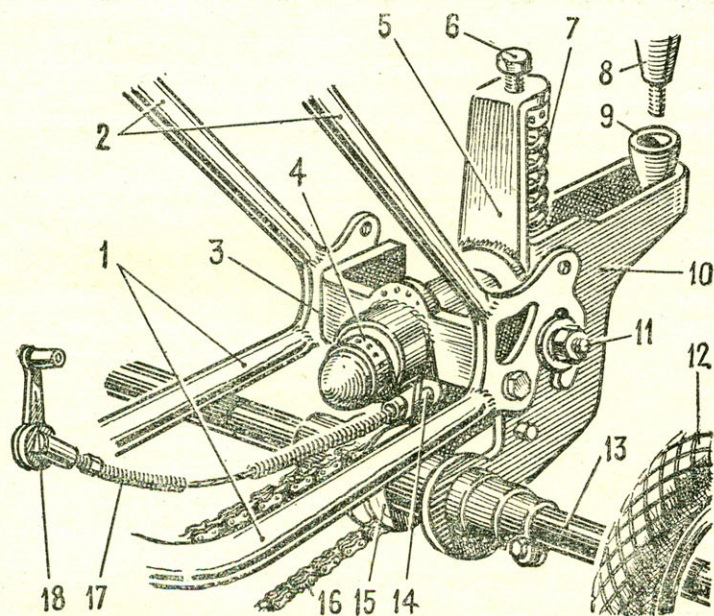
Задний мост и его крепление к раме: 1 — нижние перья задней вилки, 2 — верхние перья, 3 — скоба заднего моста, 4 — регулировочная муфта, 5 — стойка пружины, 6 — регулировочный болт, 7 — пружина, 8 — конус крепления корзины багажника, 9 — коническое гнездо, 10 — корпус заднего моста, 11 — болт крепления задней вилки к скобе, 12 — колесо, 13 — задняя ось, 14 — стопор, 15 — щечка звездочки ведущей цепи, 16 — ведущая цепь, 17 — трос стопора, 18 — рычаг стопора (располагается под седлом).
